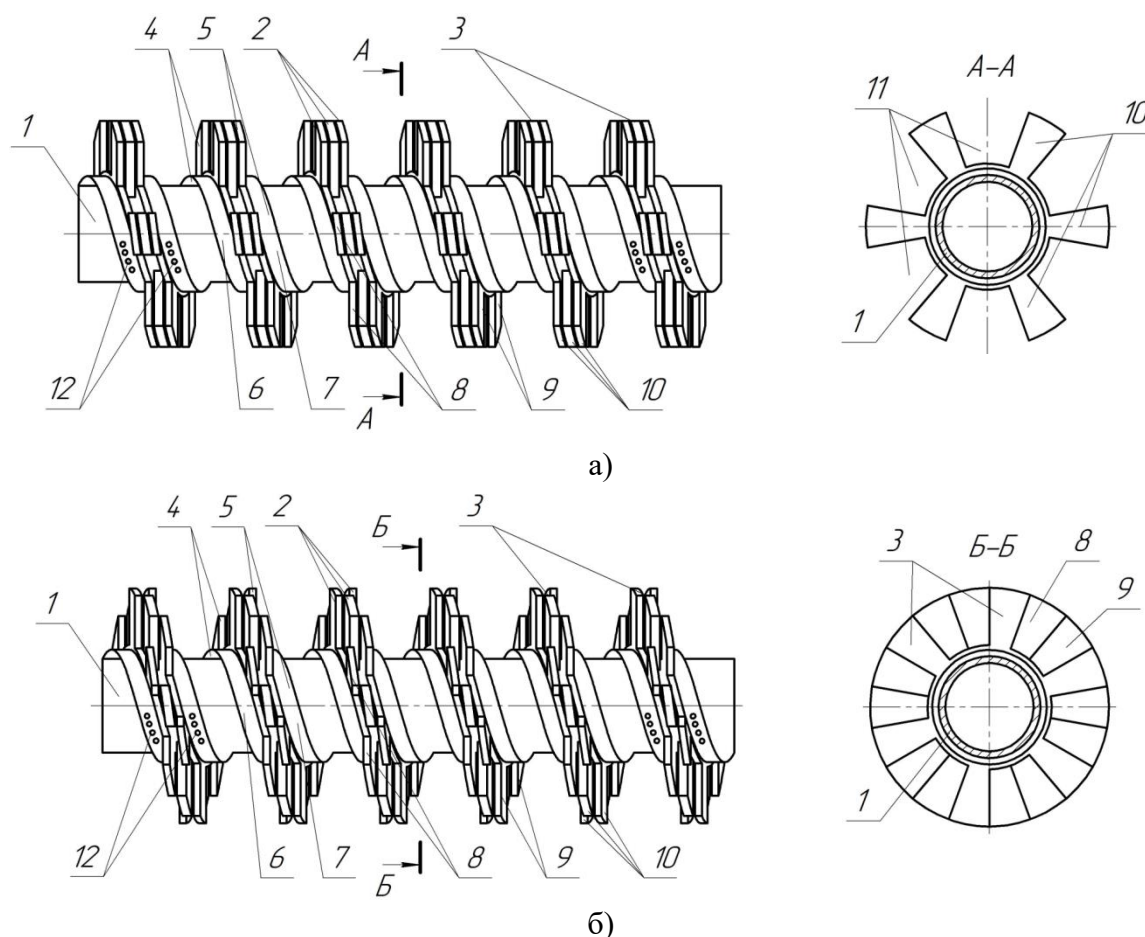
Гвинтовий робочий орган транспортера-змішувача: а) вигляд для використання у режимі змішувача; б) вигляд для використання у режимі транспортера; 1 - вал; 2 - гвинт; 3 - базова лопатева спіраль; 4 і 5 - відповідно спіралі Г-подібної форми; 6 і 7 - відповідно внутрішні суцільні циліндричні частини спіралей 4 і 5; 8 і 9 - відповідно зовнішні спіральні лопатеві частини спіралей 4 і 5; 10 - лопаті; 11 - зазор між лопатями; 12 - кріпильні гвинти
